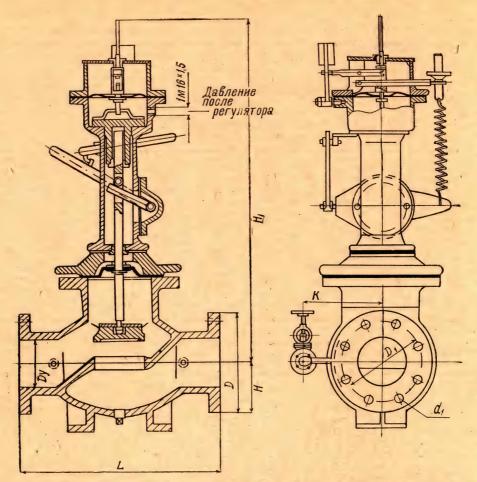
Предохранительный запорный клапан с пружине ой нагрузкой для отключения потока при повышении давления газа типа ПК-150, ПК-200 и ПК-300. Конструкция клапанов с пружинной нагрузкой ПК-80 и ПК-100 аналогична рис. 9.35.
